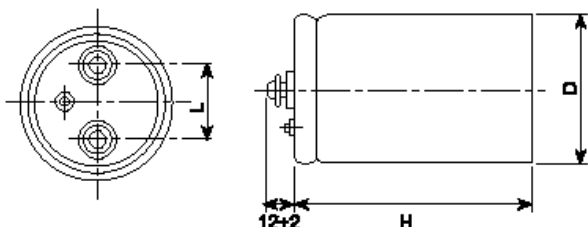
Вид корпусу конденсаторів типу К50-16
